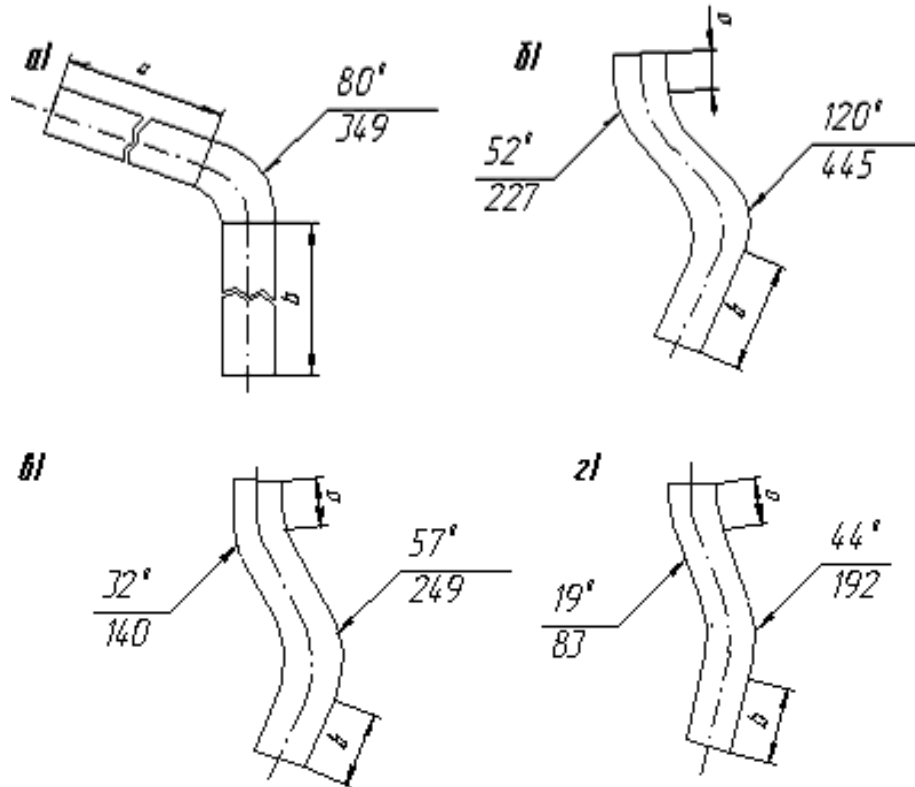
Схема для гнуття трубчатих заготовок для стінки котла
